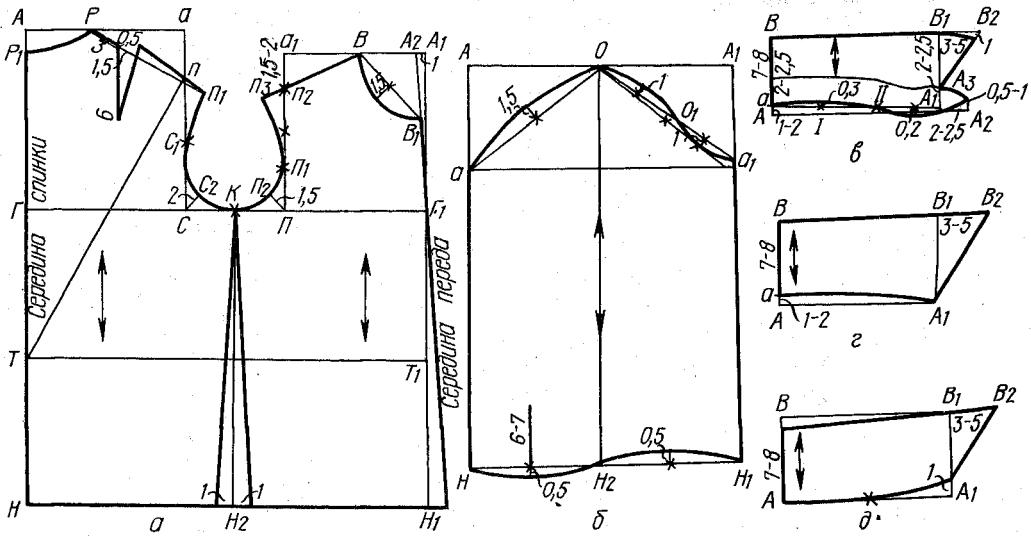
Основной чертеж верхней сорочки для мальчика:
